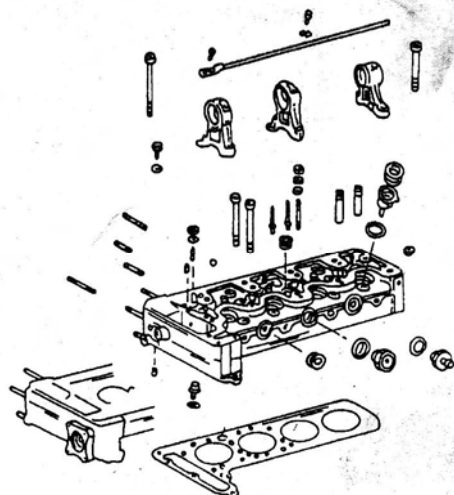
Детали блока цилиндров без кривошипно-шатунного механизма и поршней.
